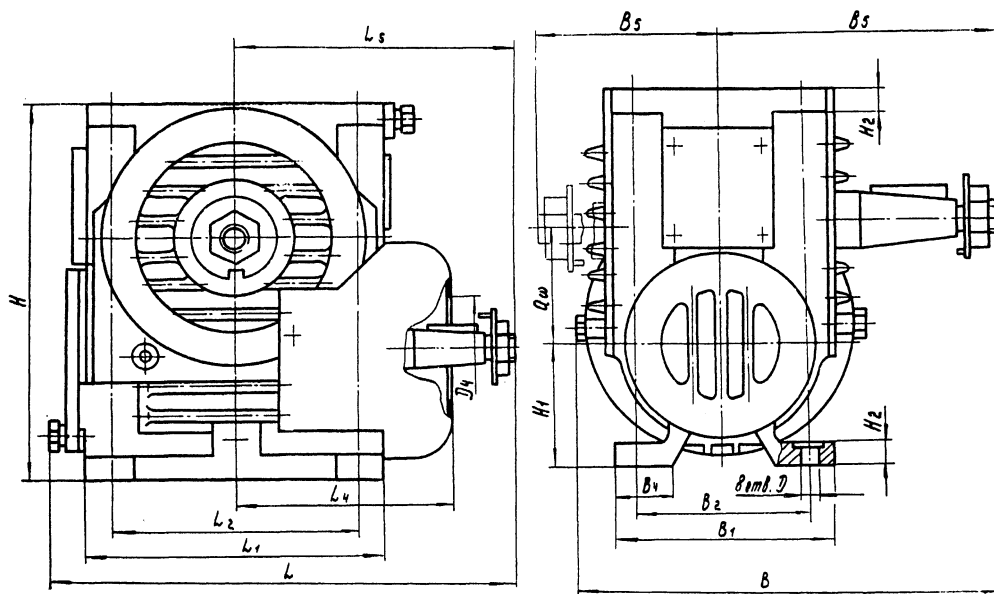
П7 Габаритные и присоединительные размеры редукторов Ч-100, Ч-125, Ч-160
